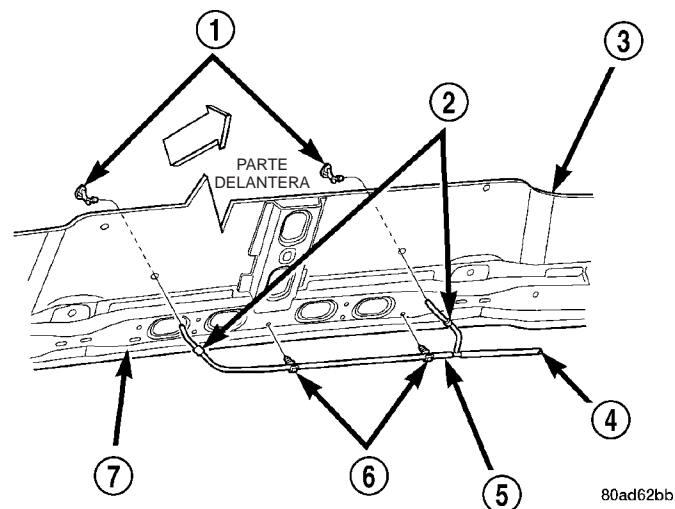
Desmontaje e instalación de boquillas del lavador delantero
